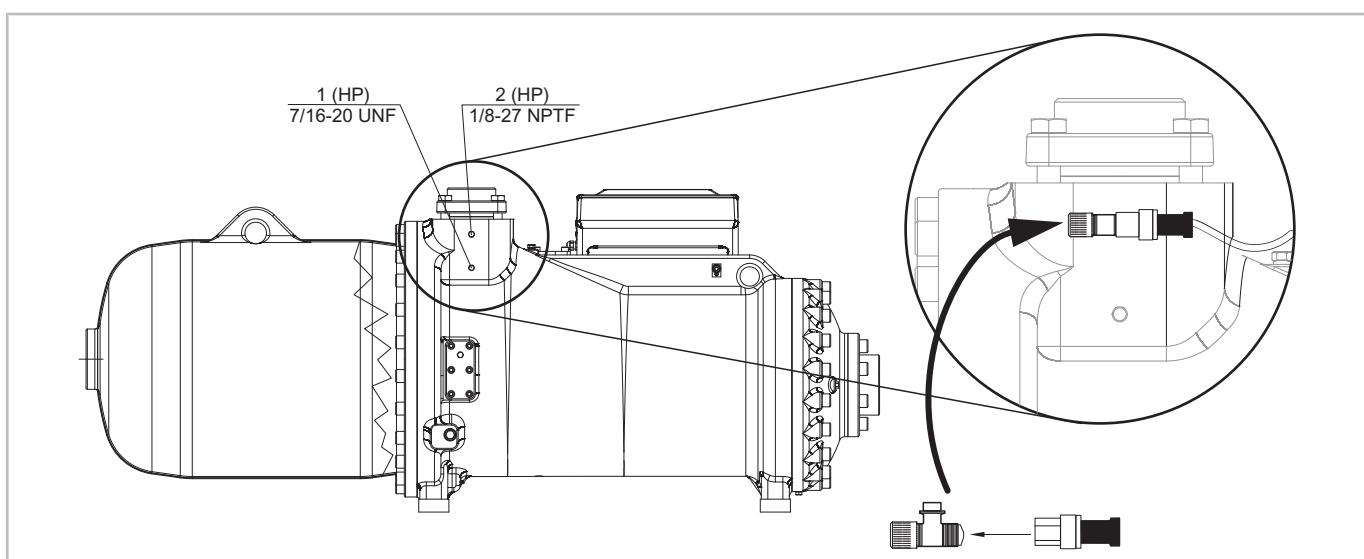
CS.95-Verdichter: Montage des Hochdruckmessumformers
